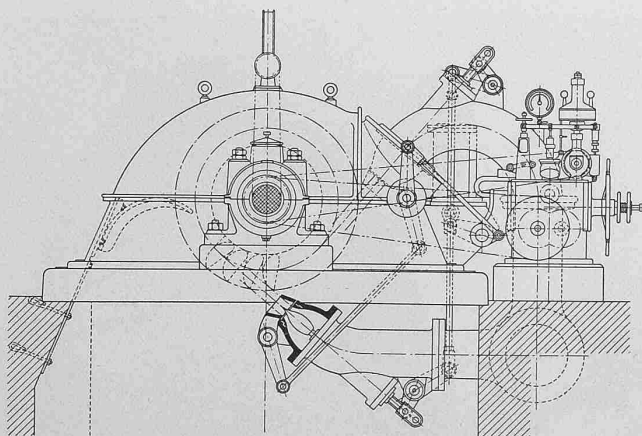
2000 PS-Pelton-Turbine von Theodor Bell & Cie.
